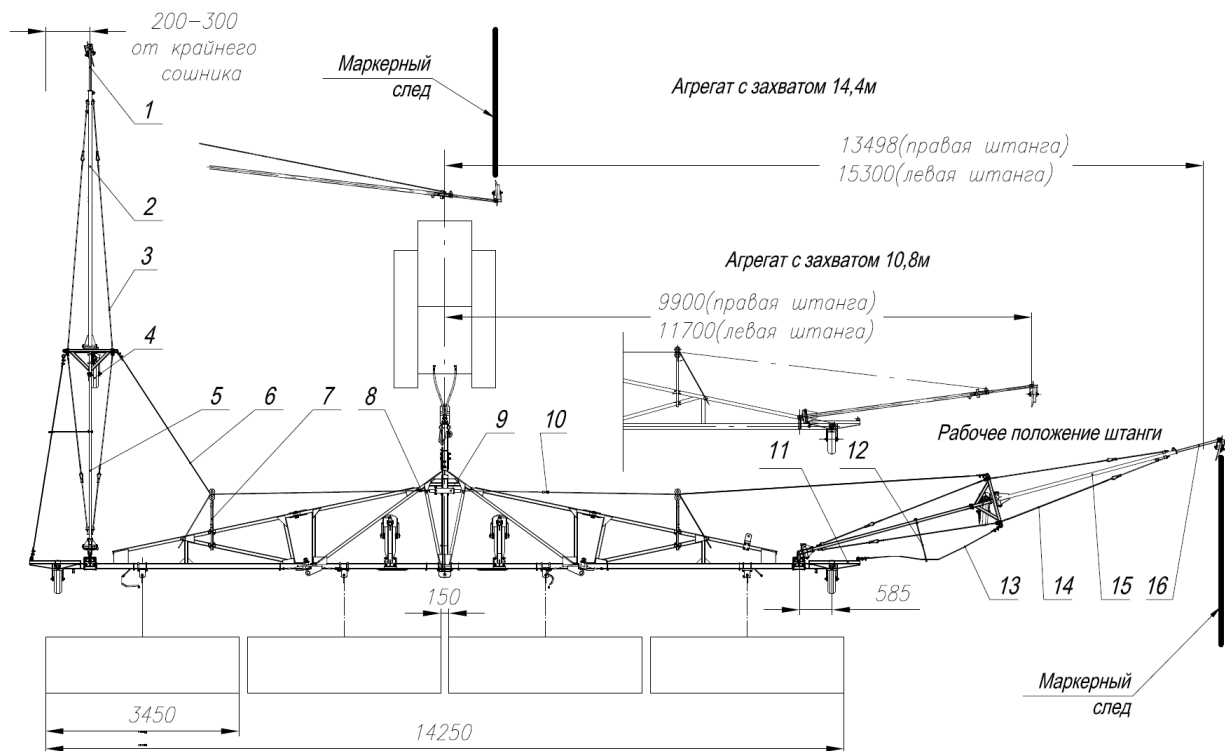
Схема установки маркера для 4-х и 3-х сеялочного агрегата.
